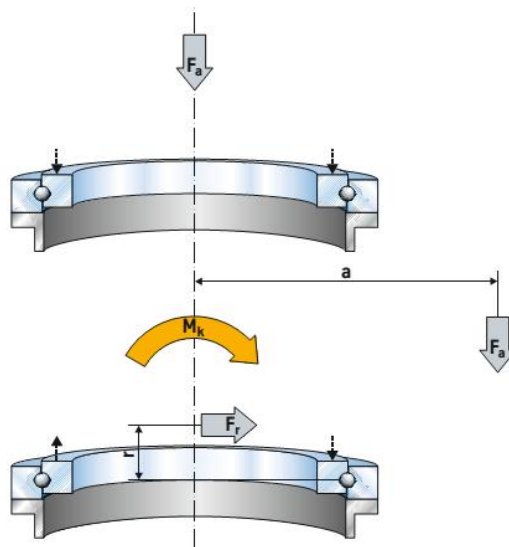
Esfuerzos actuantes sobre el rodamiento
